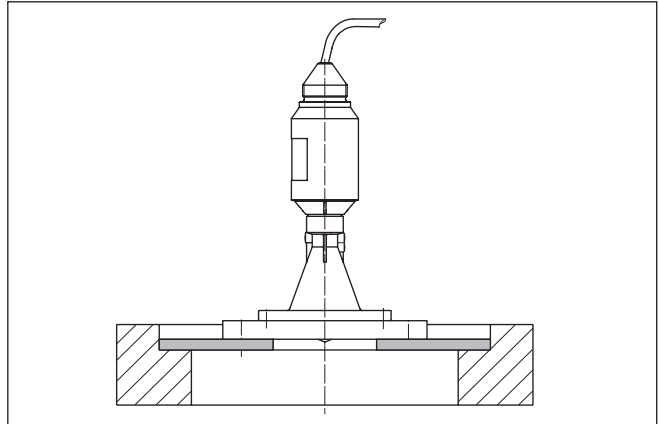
Montage mittels des Adapterflansches, z. B. auf einer Schachtabdeckung.
